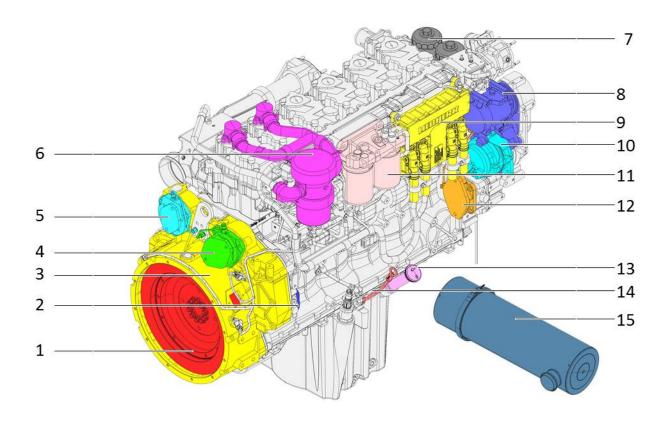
Componentes del motor diésel D936 A7 SCR / Vista de la derecha
